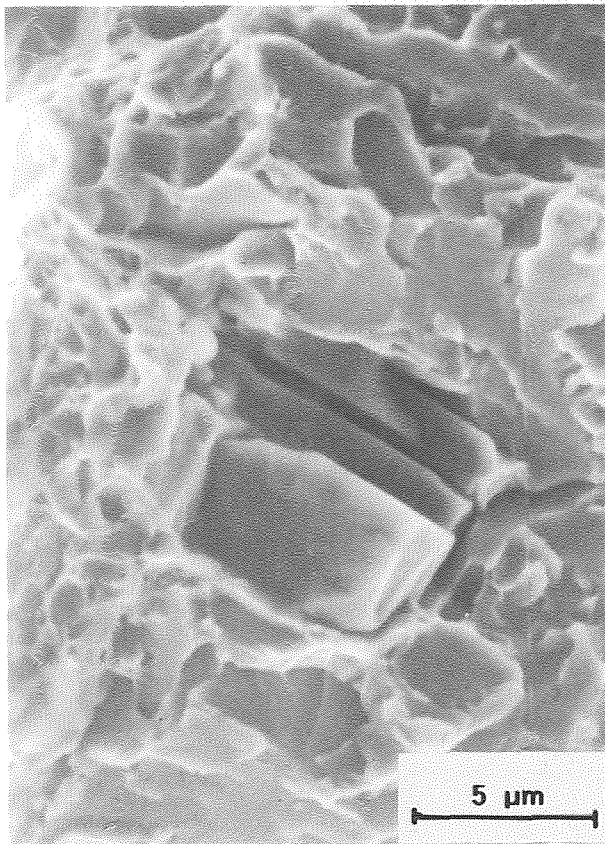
Partícula rota de TiN que no ha originado la fractura frágil de la matriz circundante.
